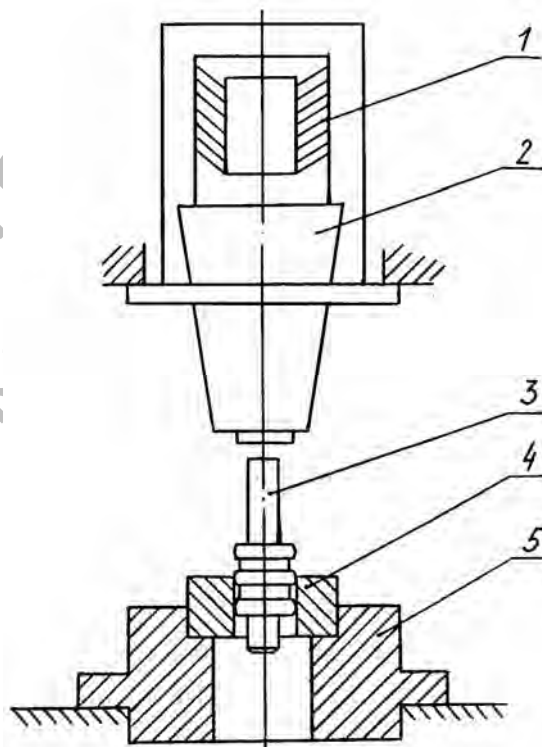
Схема колебательной системы для дорнования отверстий: 1 – преобразователь; 2 – волновод; 3 – дорн; 4 – деталь; 5 – опора
